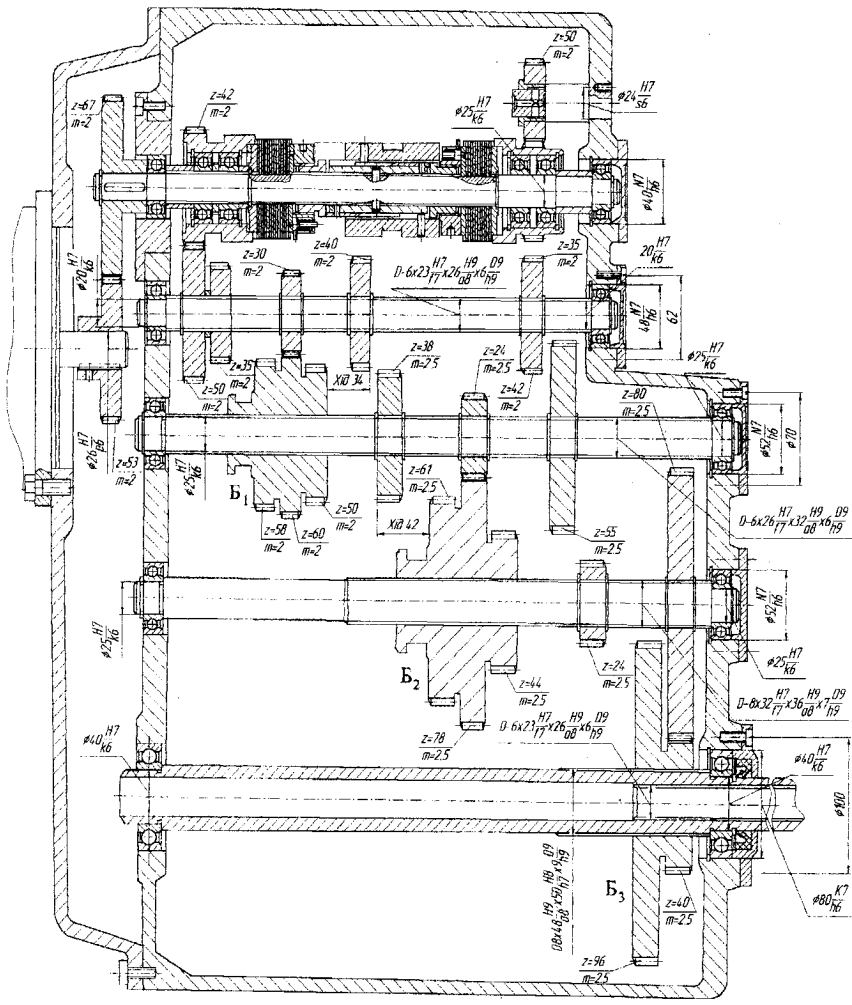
Коробка швидкостей фрезерних верстатів
